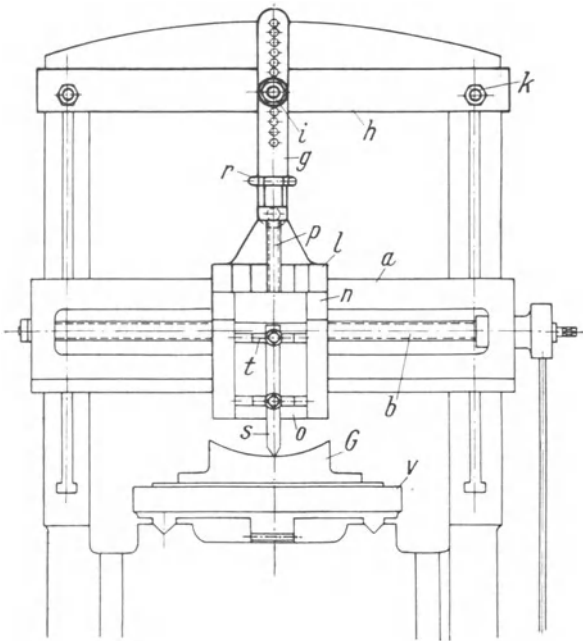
Vorrichtung zum Hobeln hohler Flächen.
